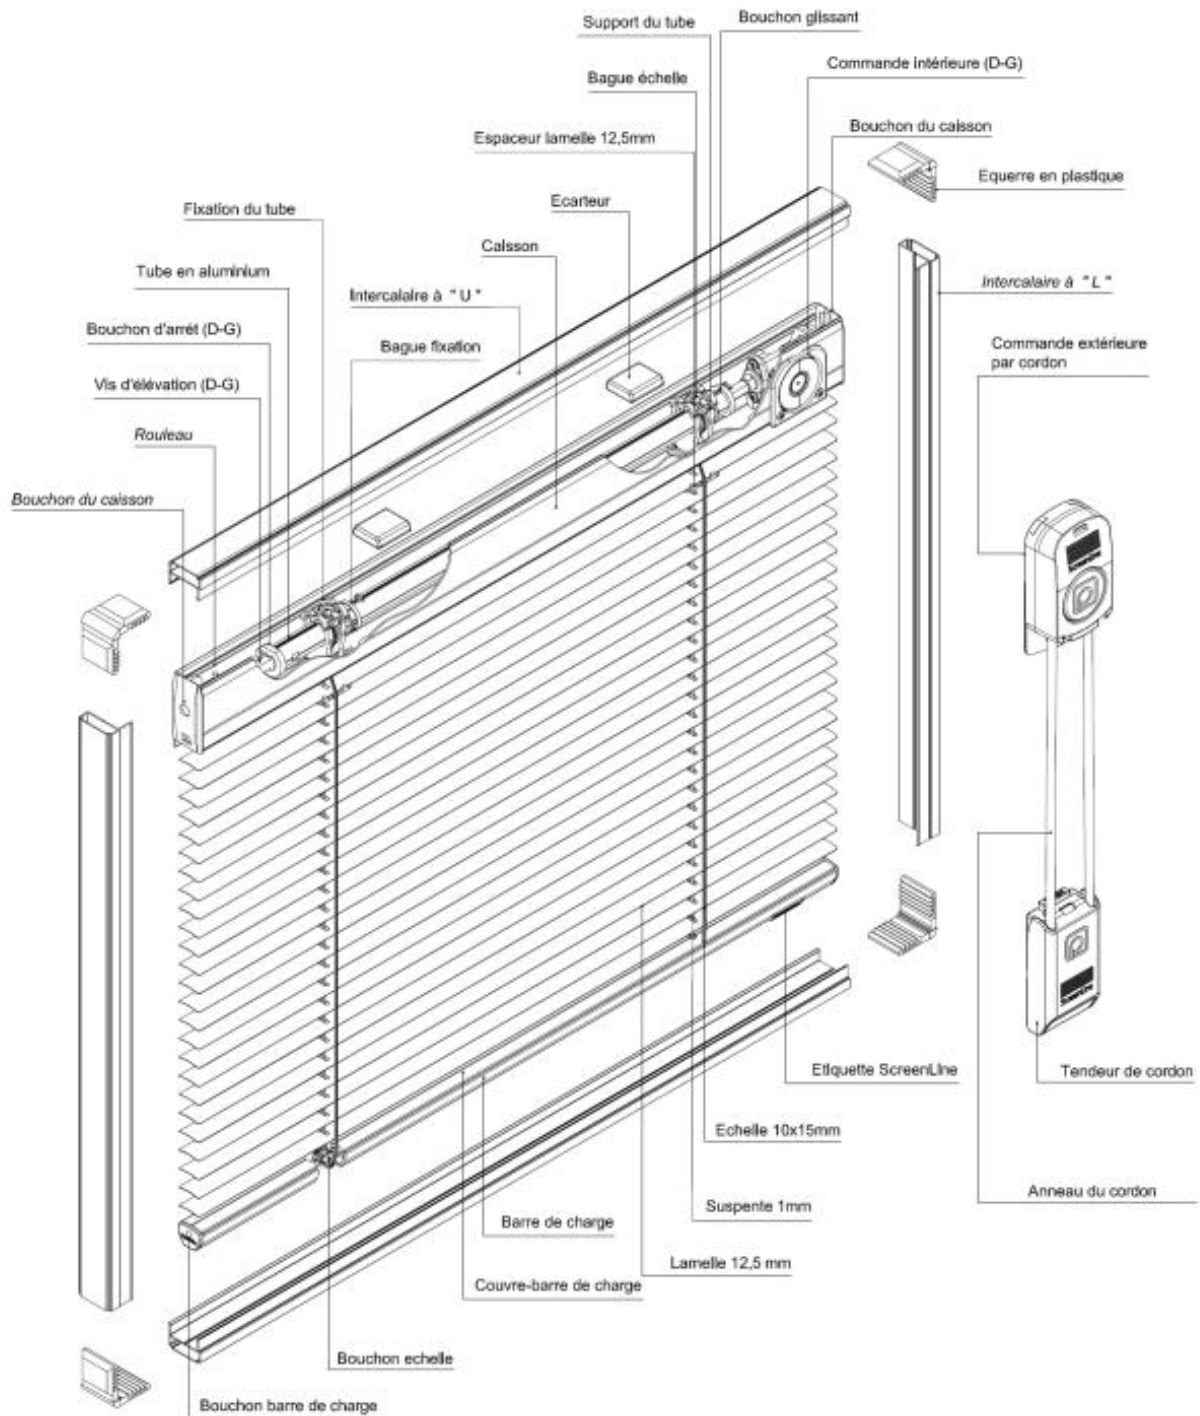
Vue d'ensemble éclatée avec espaceur aluminium
